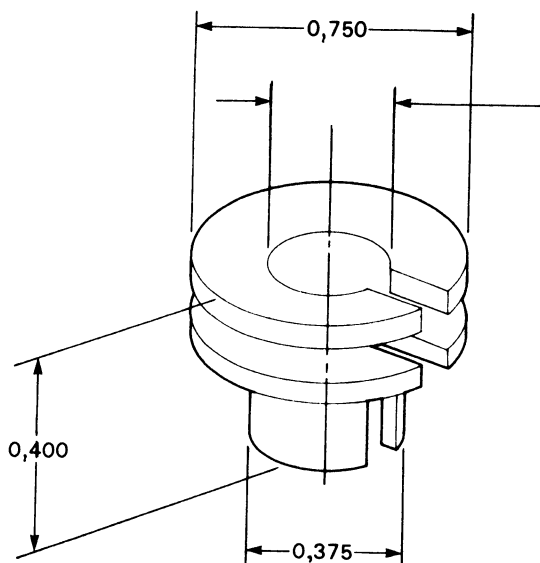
Радиатор для корпуса типа ТО-5. (Все размеры приведены в дюймах.)
